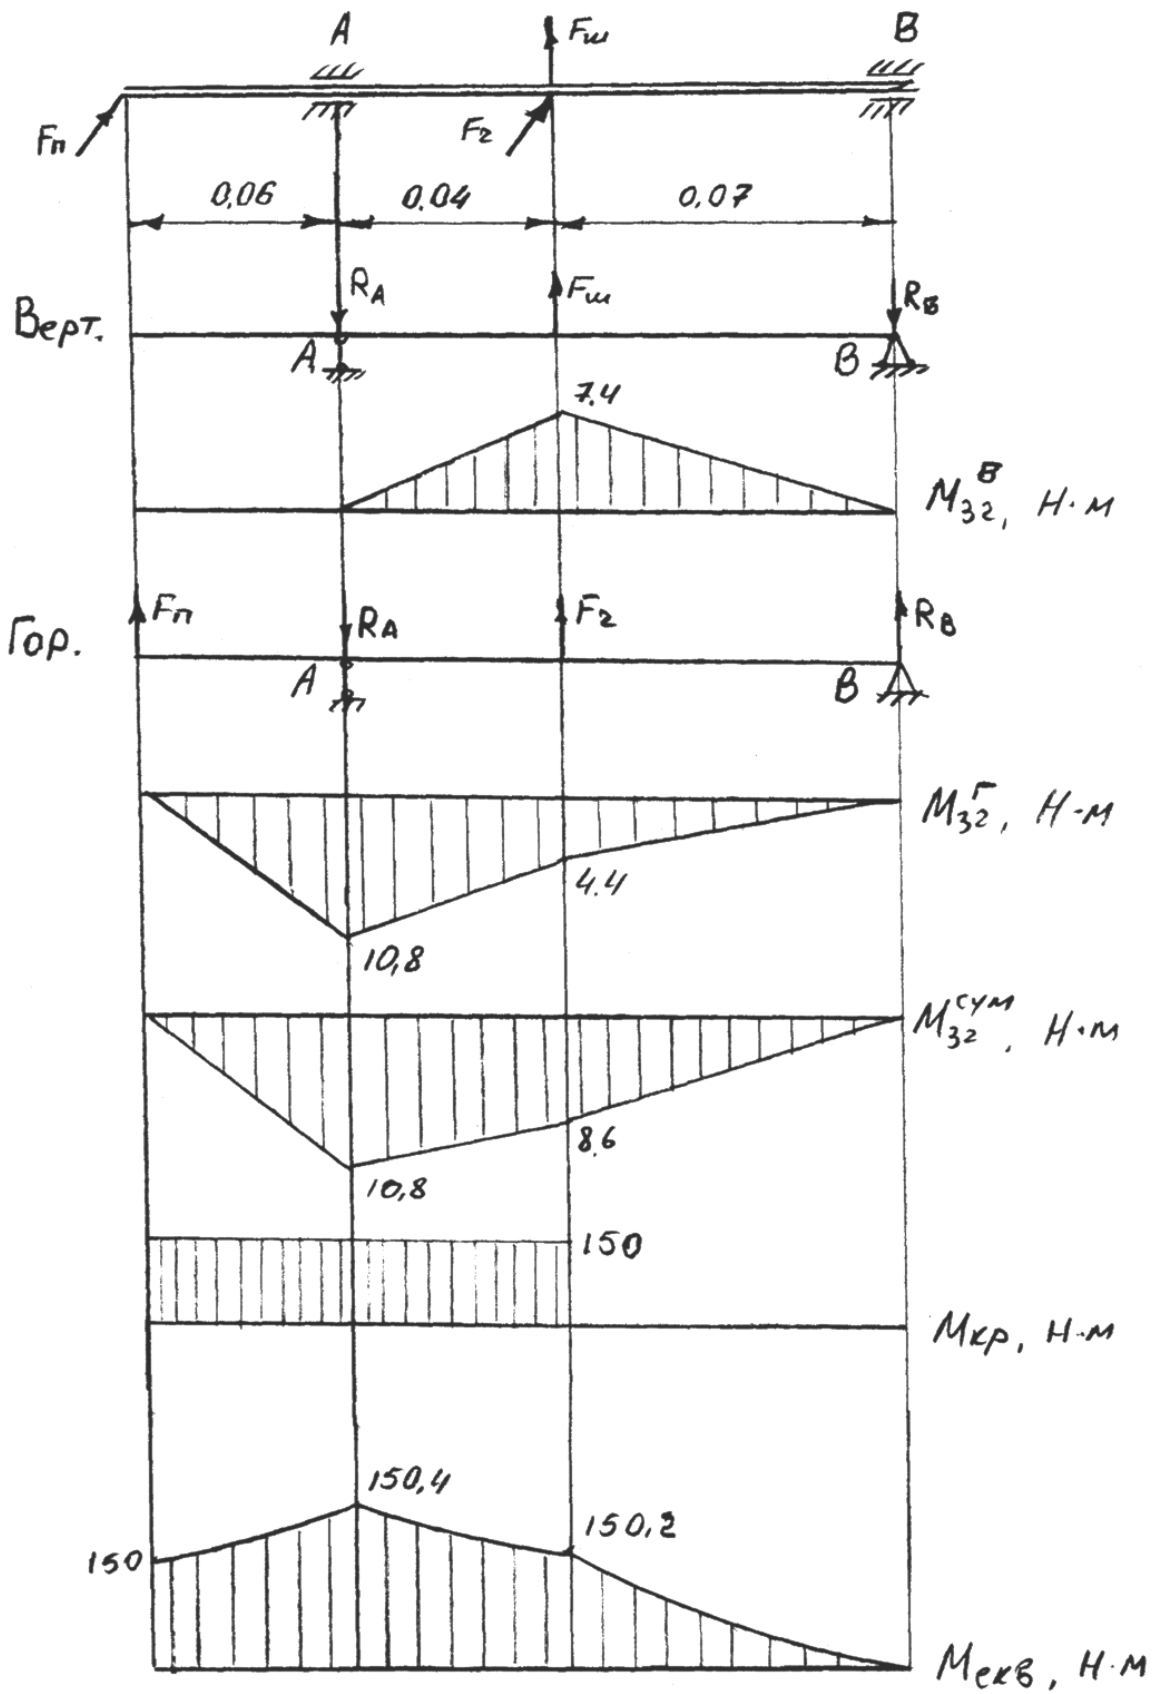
Розрахункова схема валу кривошипно-шатунного механізму
